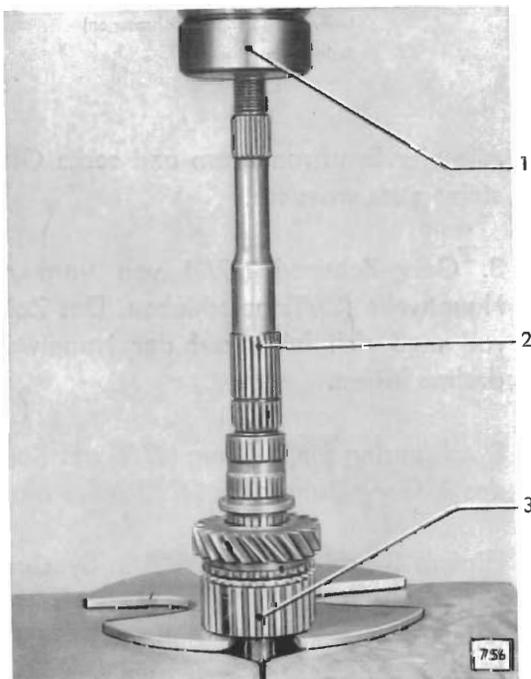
Synchronkörper auf Hauptwelle aufpressen
